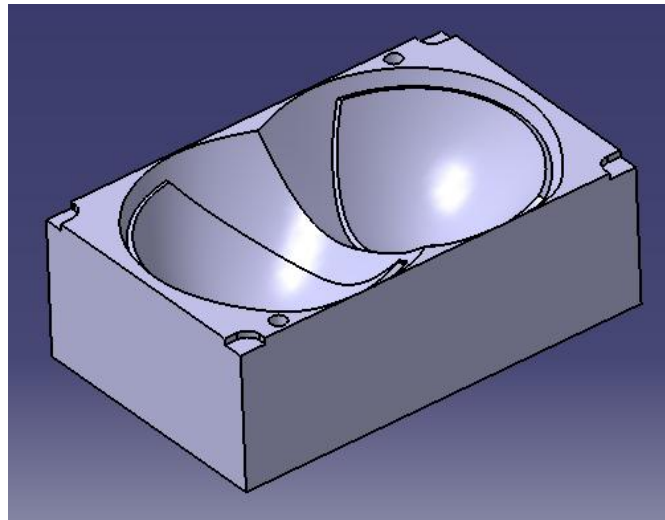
Diseño CAD 3D del molde hembra
